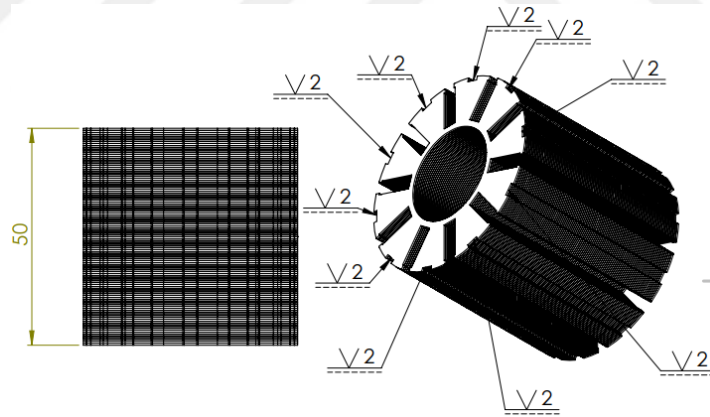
M400-50A silisli sacın rotor paketi için CAD çizimi
